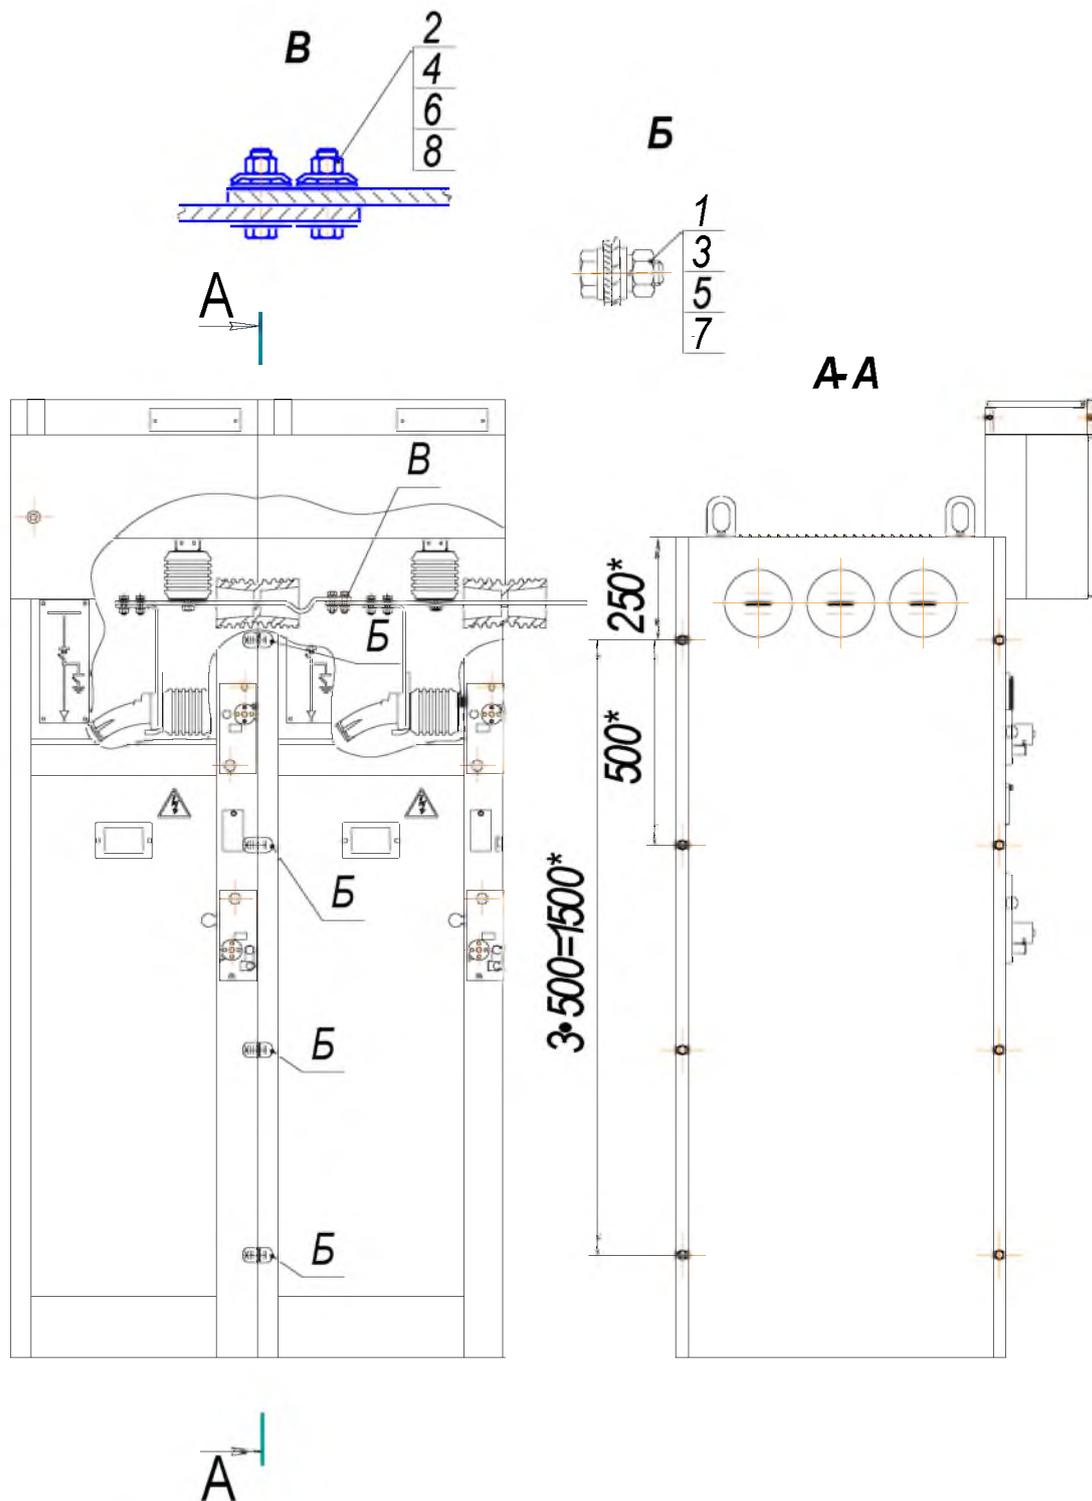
Стыковка камер КСО-СЭЩ по сборным шинам
